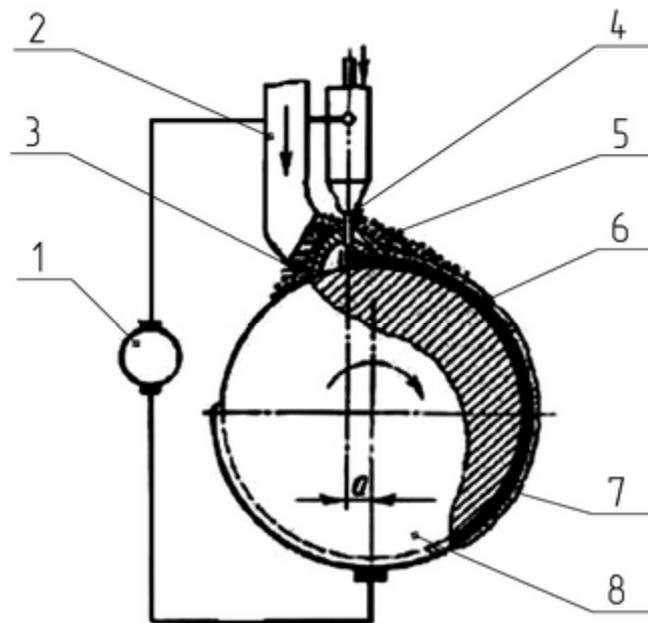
Схема автоматической наплавки под слоем флюса:
